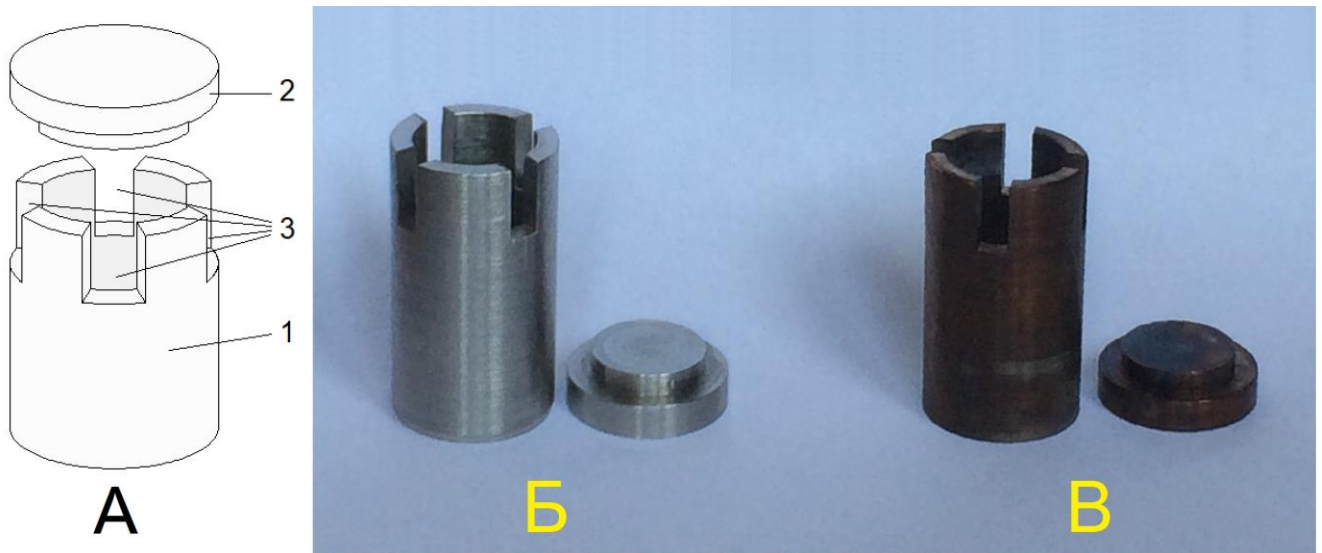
Дополнительный внутренний контейнер для обработки твердого образца ВФ [154]: А – схематическое изображение (1 – корпус контейнера; 2 – крышка; 3 – окна для обеспечения проникновения флюидной фазы – паровой или СК); Б – контейнер до обработки; В – С контейнер, обработанный в среде ВФ (400°C, плотность флюида 0.25 г/см³)
